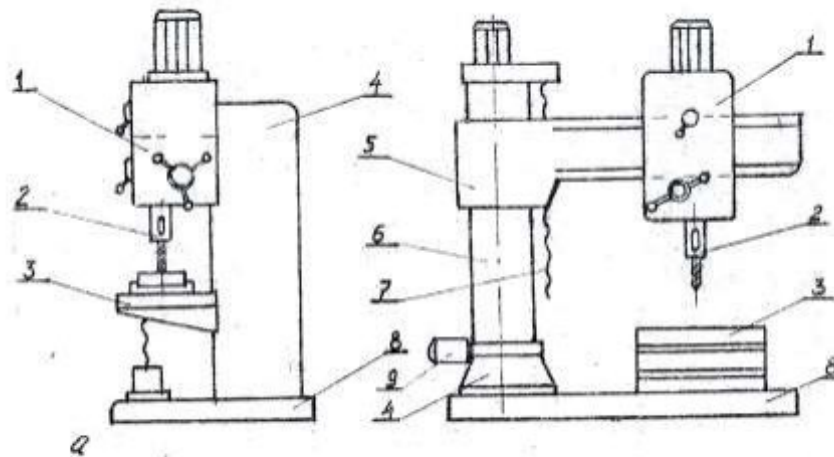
Вертикально-свердлувальний (а) та радіально-свердлувальний верстати (б).
